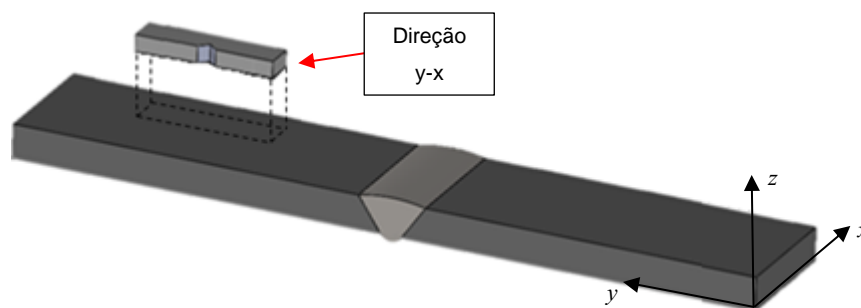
Orientação do entalhe em relação a junta soldada
